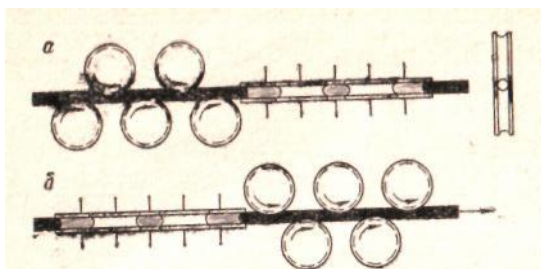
Схема правильного пристрою багато роликового верстата: а - вид збоку; б - вигляд зверху.
